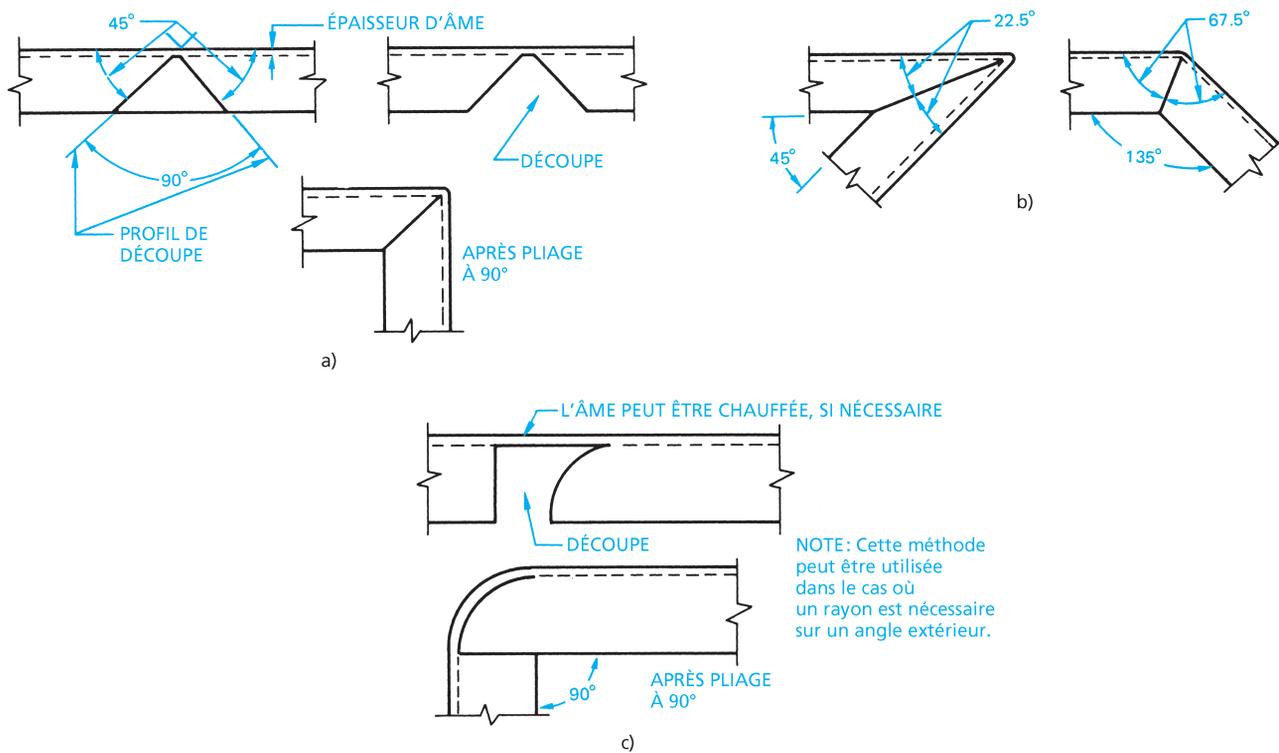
■ Préparation des assemblages par coupage et formage.
